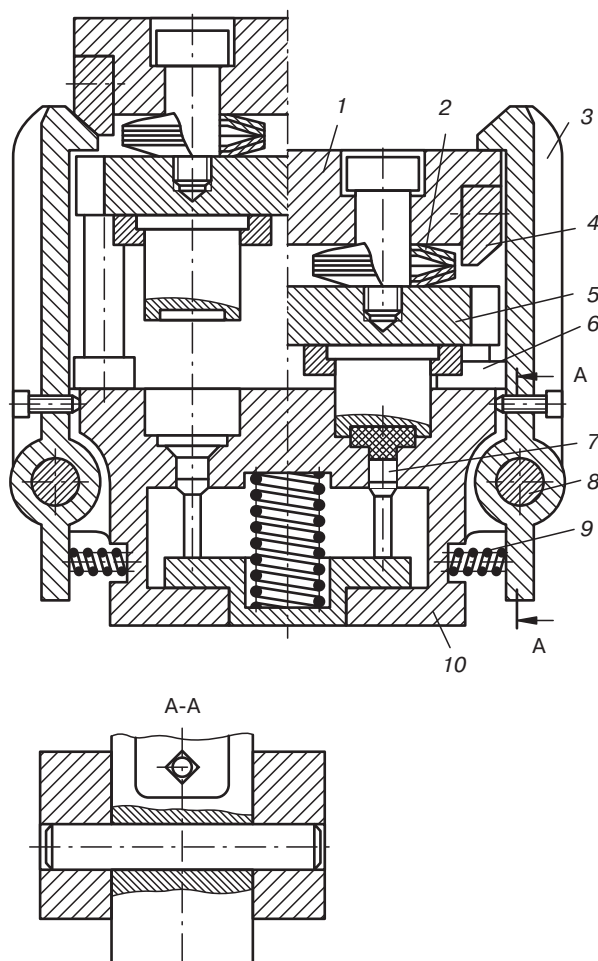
Схема выносной пресс-формы прямого прессования с рычажным замковым устройством
